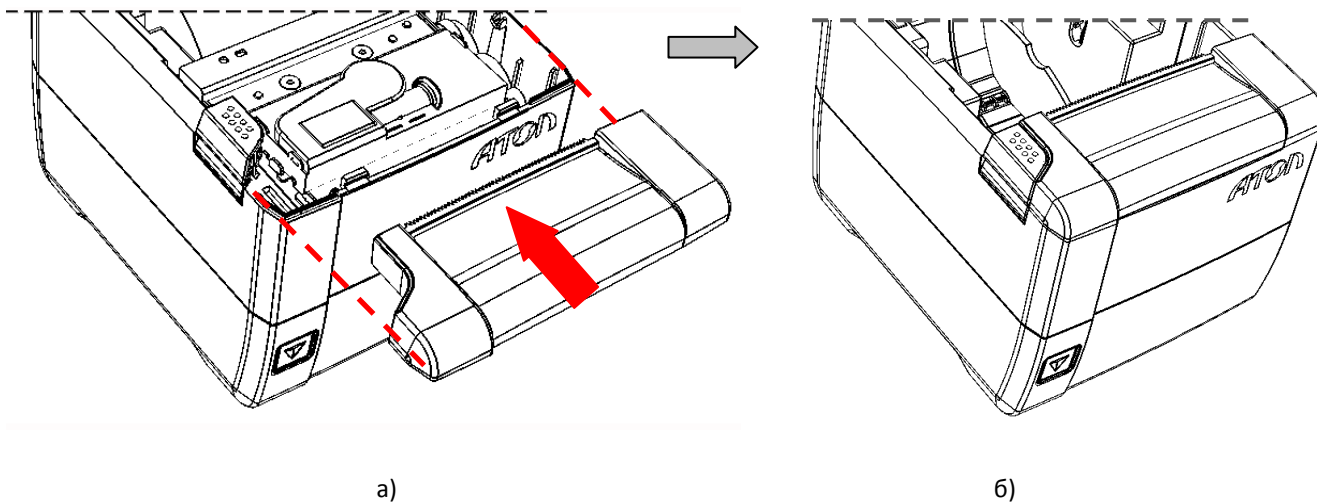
Установка крышки ТПМ: а) совместить крышку с корпусом изделия, надавить на крышку до упора; б) крышка ТПМ закрыта
